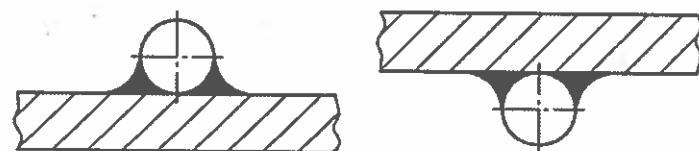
Форма галтели (закругления) припоя в местах плавного перехода от одной поверхности соединяемых деталей к другой поверхности соединяемых деталей
